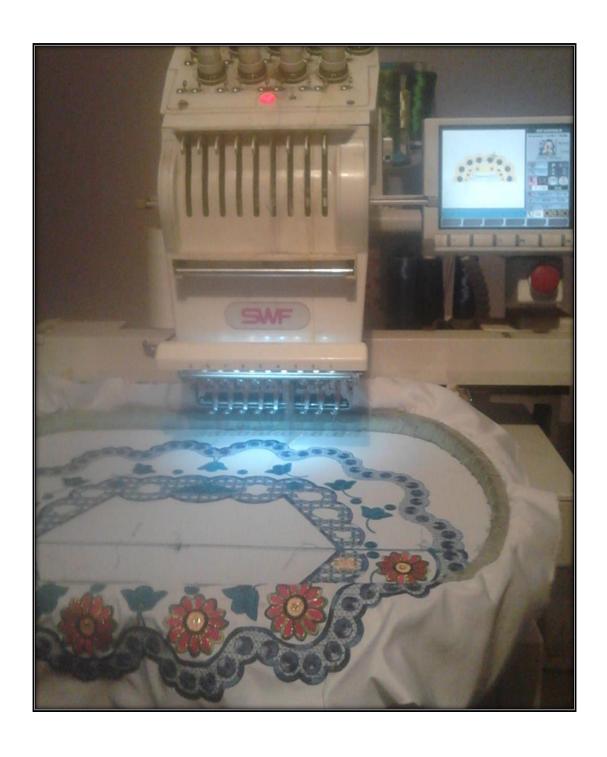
Máquina bordando el diseño seleccionado Elaborado por: Rubí Cusin
